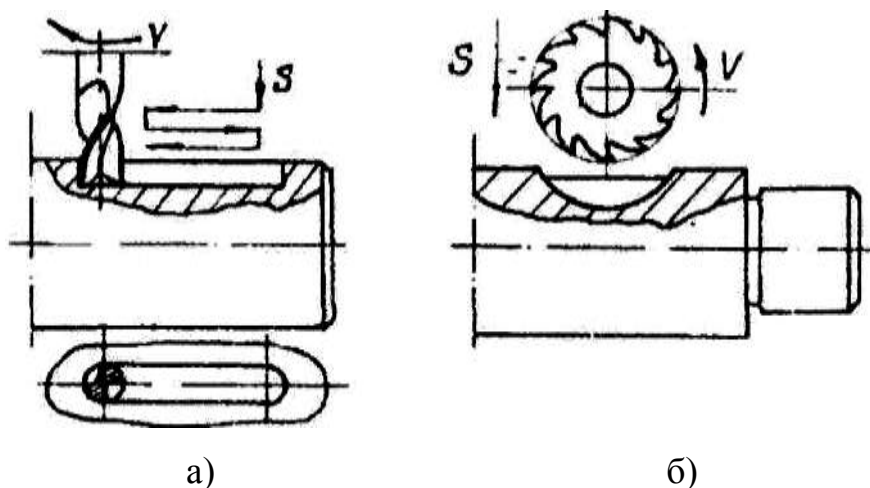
Фрезерование шпоночных канавок концевыми фрезами под призматические шпонки (а) и дисковыми фрезами под сегментные шпонки (б)
